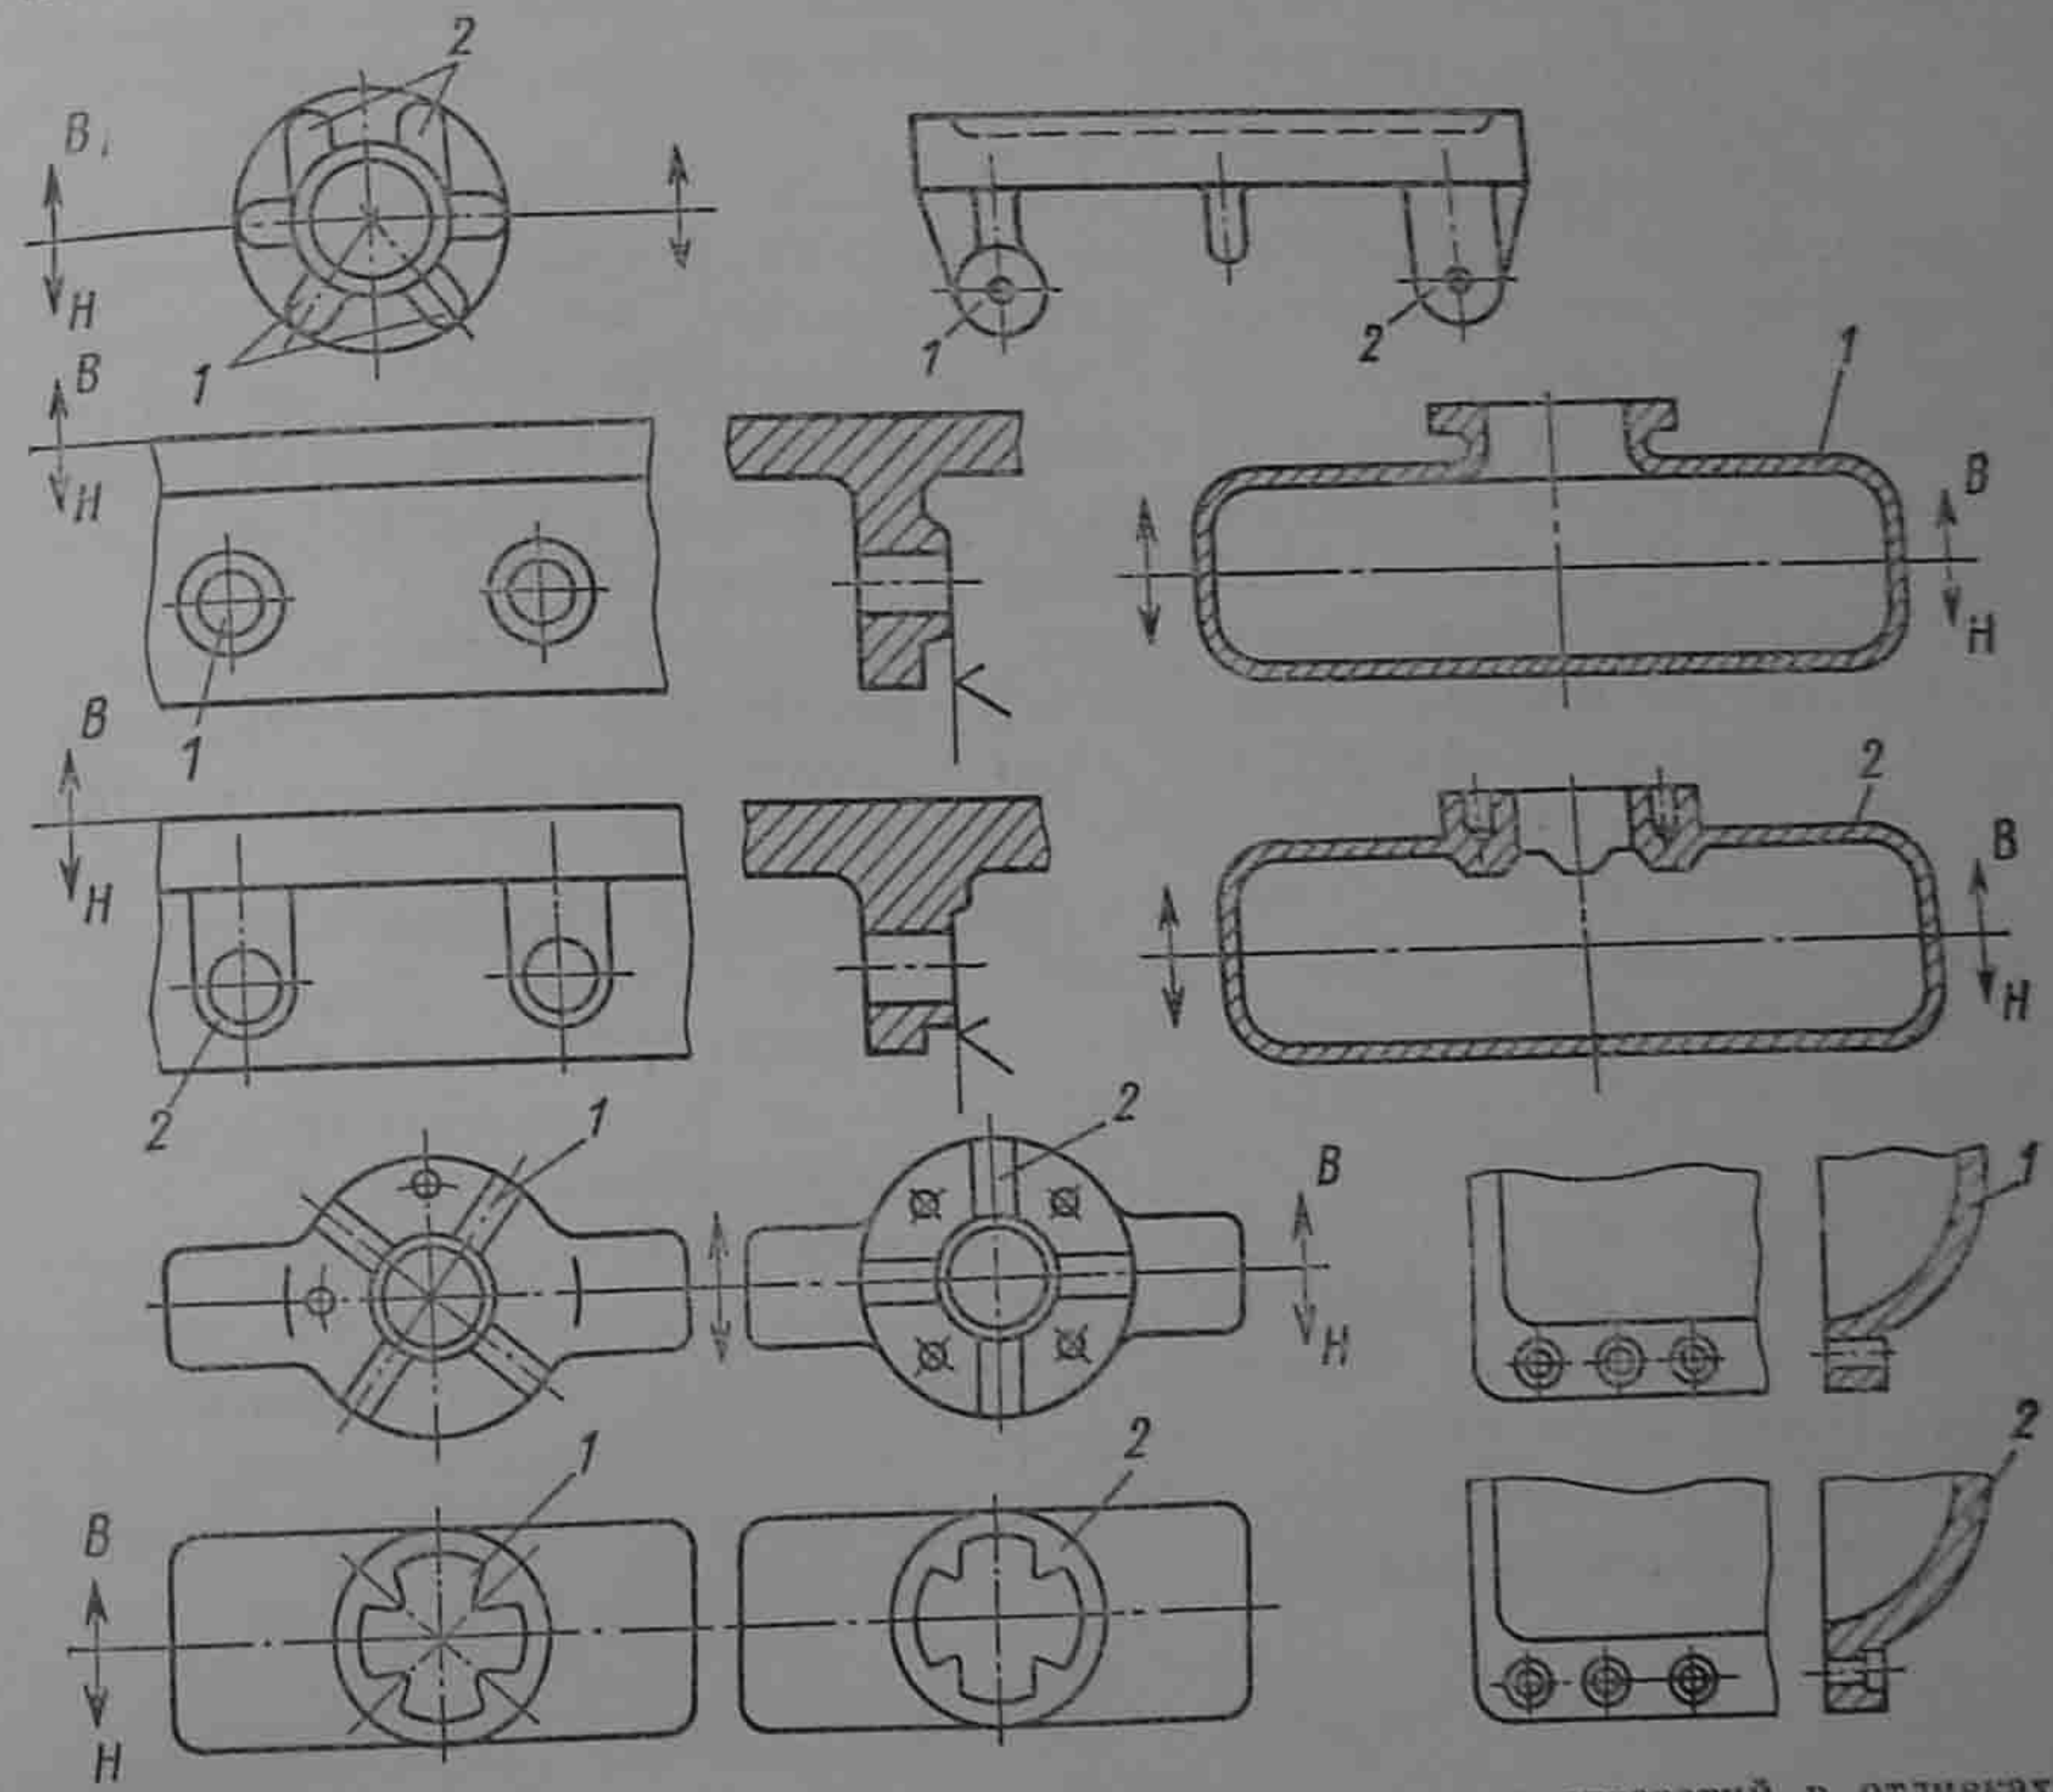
Примеры оформления бобышек, ребер, фланцев и отверстий в отливках, обеспечивающих более легкое изготовление детали:
